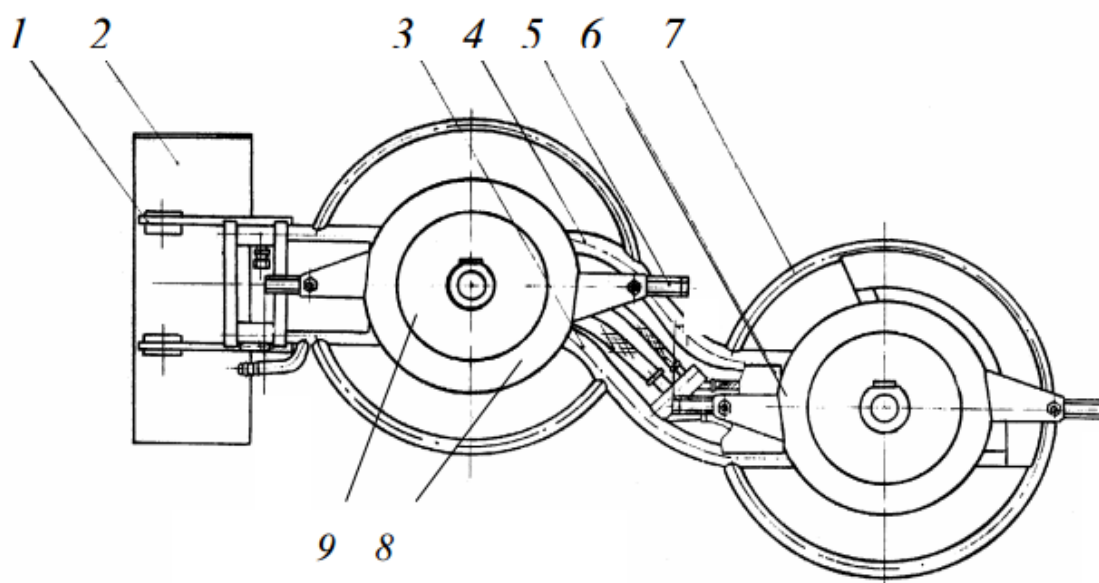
Конструктивная схема двухроторного рабочего органа косилки
